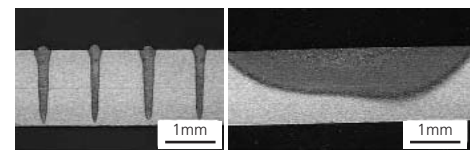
Querschliffe von Faserlaserschweißnähten (links) und einer HLDL-Härtespur (rechts)
